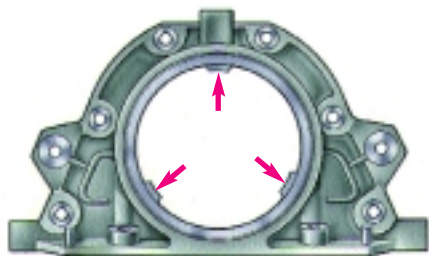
Держатель заднего сальника коленчатого вала двигателя мод. 2106-70 (стрелками указаны выступы для центрирования держателя относительно фланца коленчатого вала)
